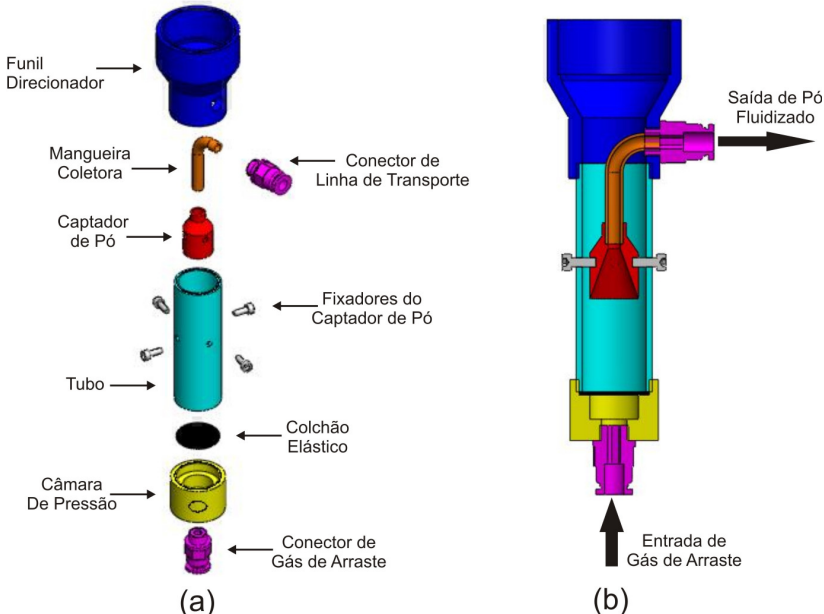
Novo Fluidizador: a) vista explodida; b) vista frontal em corte da estrutura
